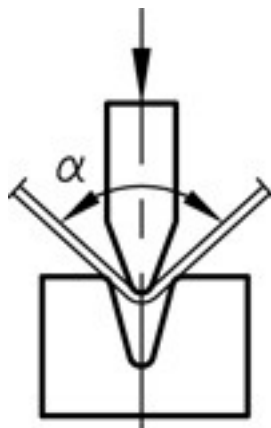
Nástroj pro ohýbání do V tvaru [20]
